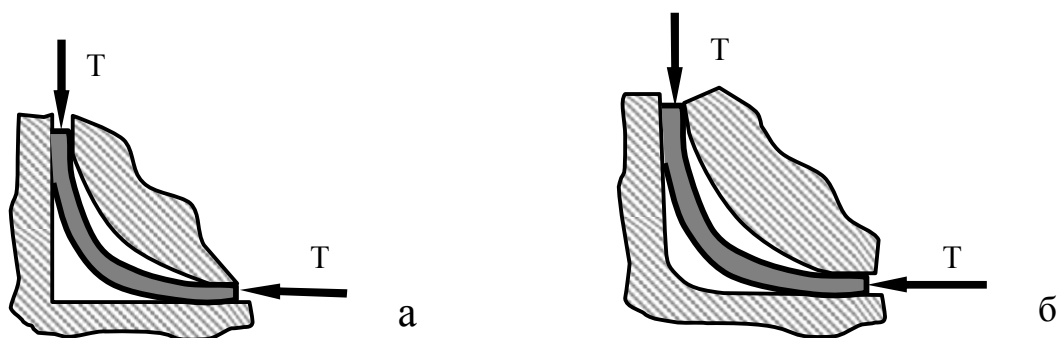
Схемы формовки угловой зоны: а – с двусторонним высвобождением; б – с высвобождением по внутреннему контуру и посадкой наружного контура
